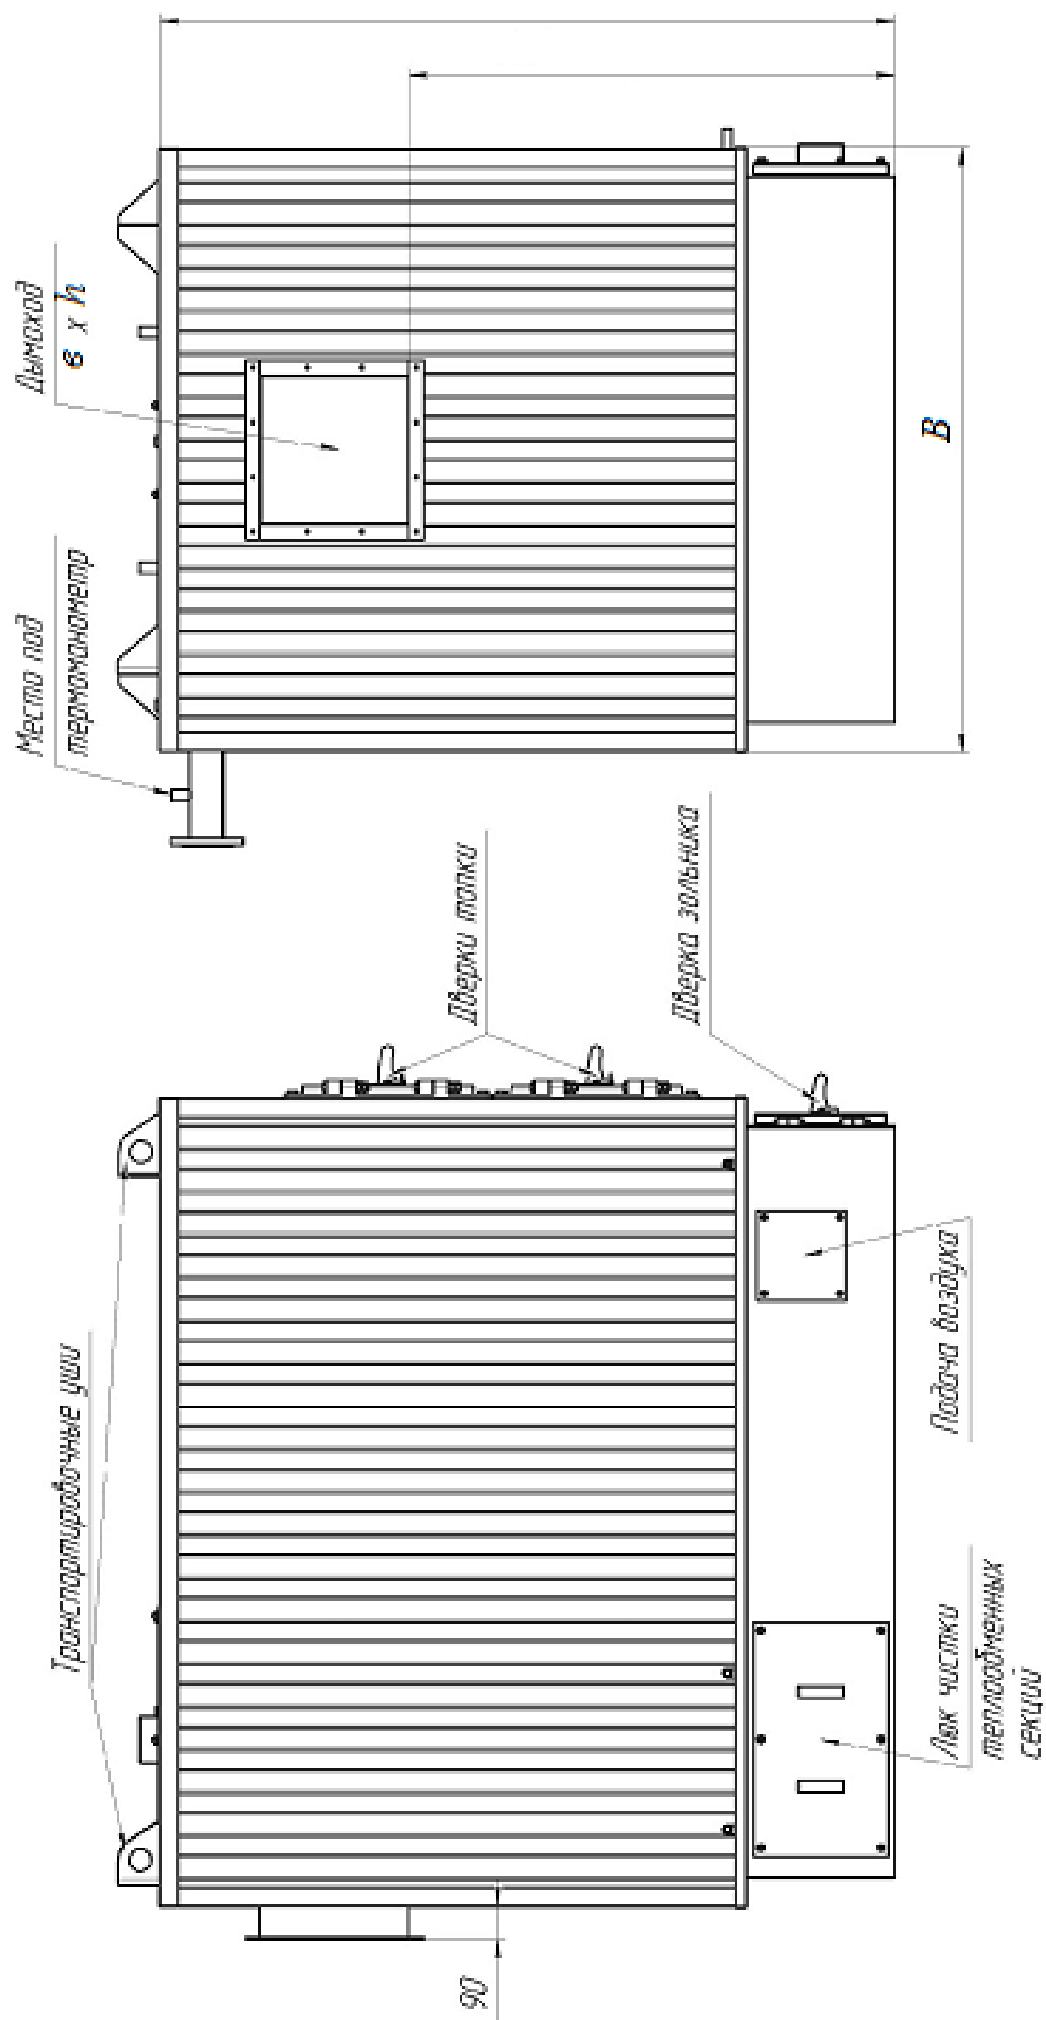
Габаритные и присоединительные размеры котла КВр.
